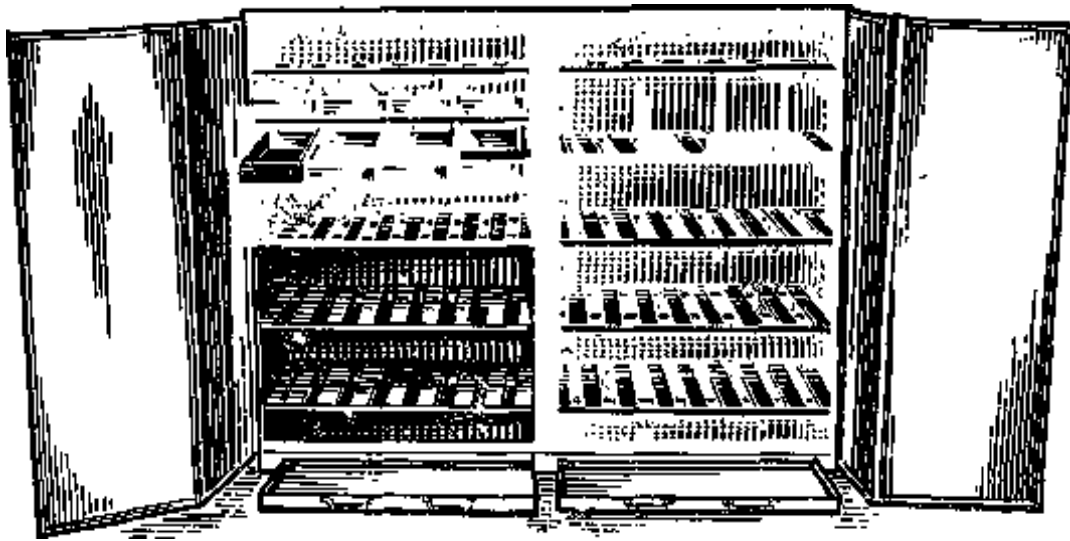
Стелаж - шафа для зберігання газового обладнання
